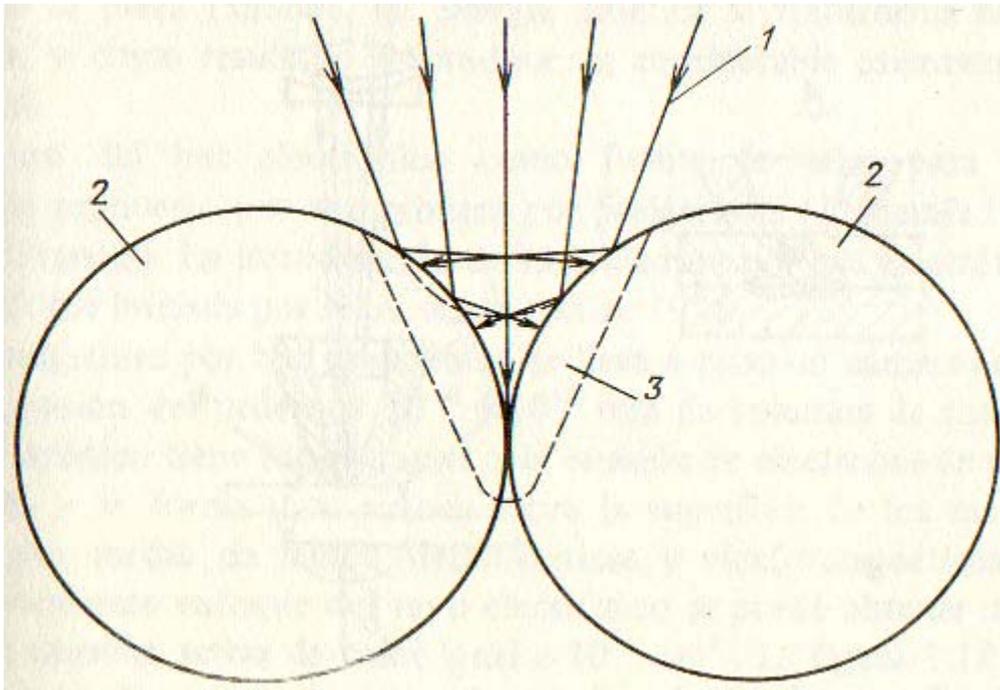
Esquema de soldadura por Rayo Láser de conductores colocados paralelamente: 1- radiación Láser; 2- hilos a soldar; 3- zona de fusión. [9]
